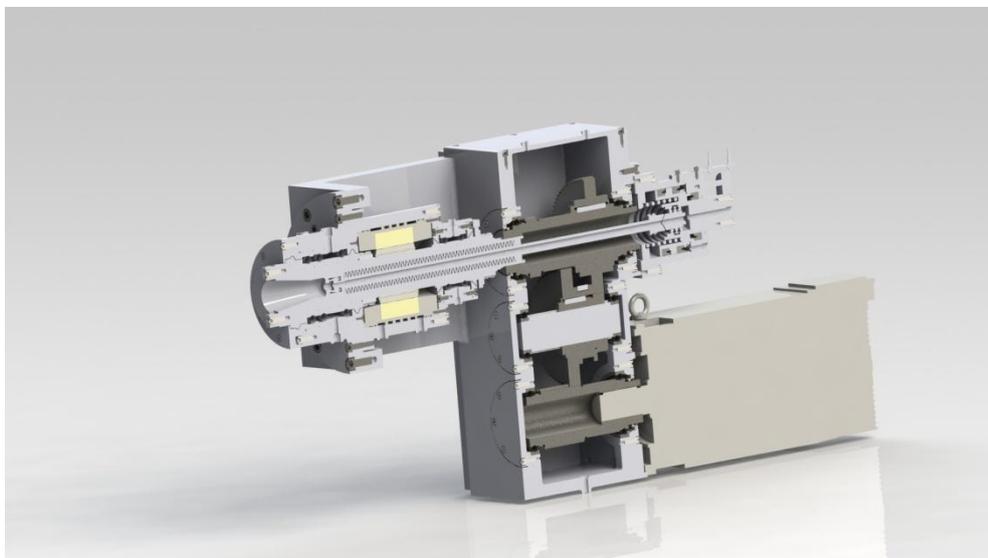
Конструкция шпиндельного узла ИР500ПМФ4 с двумя электродвигателями.
